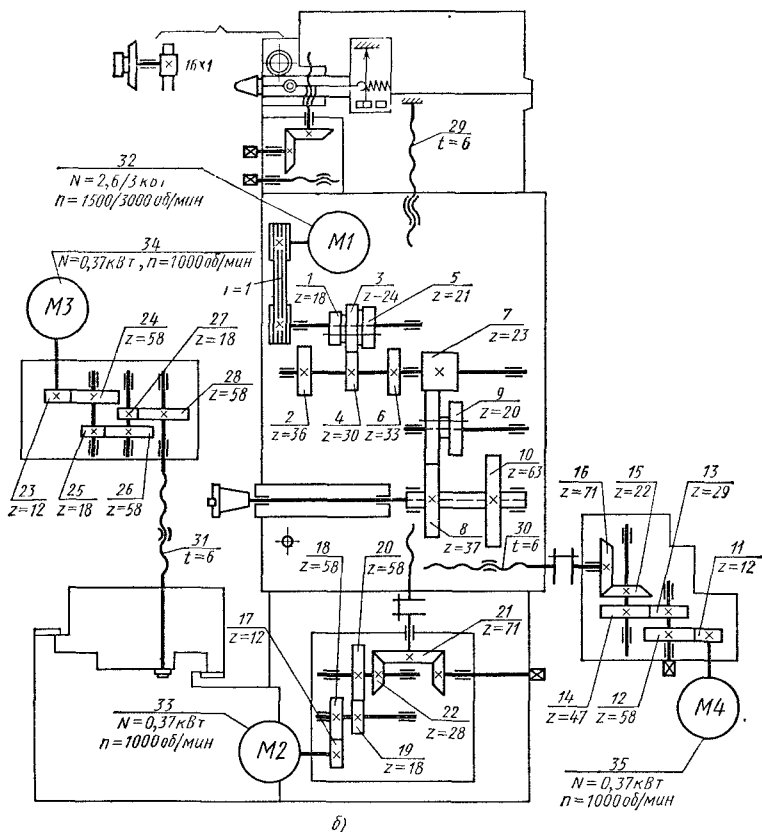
Кинематическая схема электрокопирующего фрезерного полуавтомата мод. 6Б443Г
